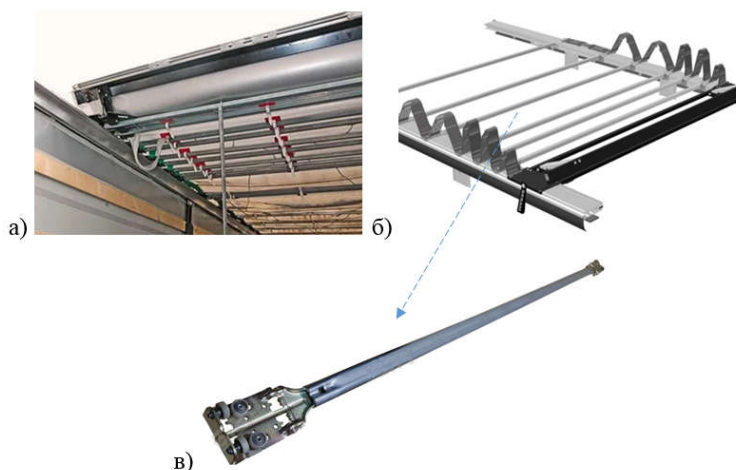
Крыша сдвижная - а, механизм складной крыши полуприцепа - б, кронштейн роликовой тележки в сборе с поперечиной - в
